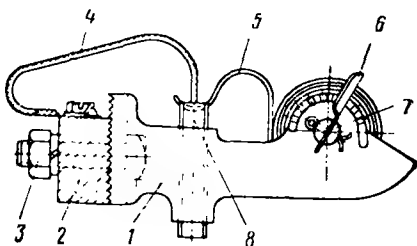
Щеткодержатель преобразователя НБ-429А:
